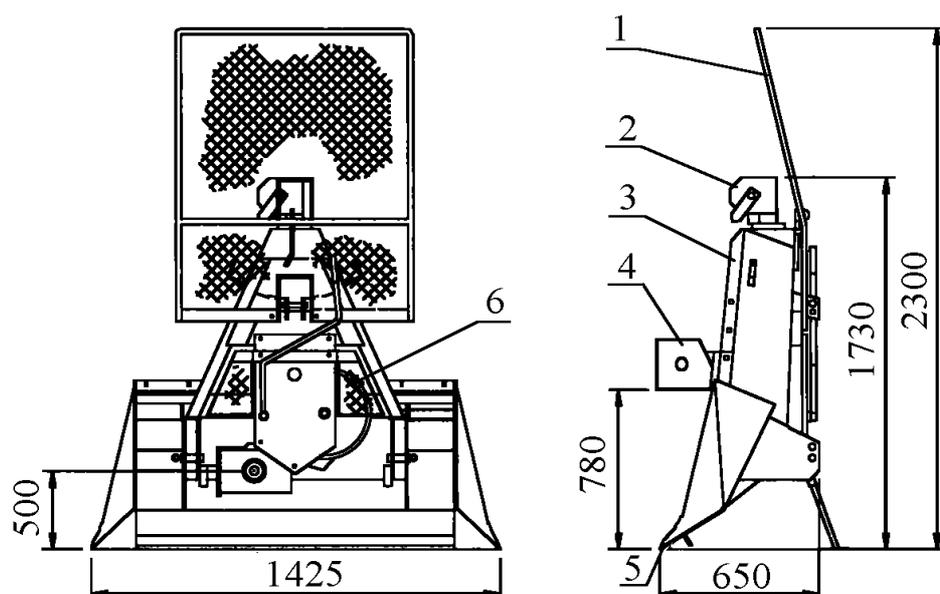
Трелевочное приспособление трелевочной машины ТТР-401: 1 – защитное ограждение трелевочного приспособления; 2 – верхний канатонаправляющий блок; 3 – упорный щит; 4 – нижний канатонаправляющий блок; 5 – откидывающаяся опора; 6 – лебедка
